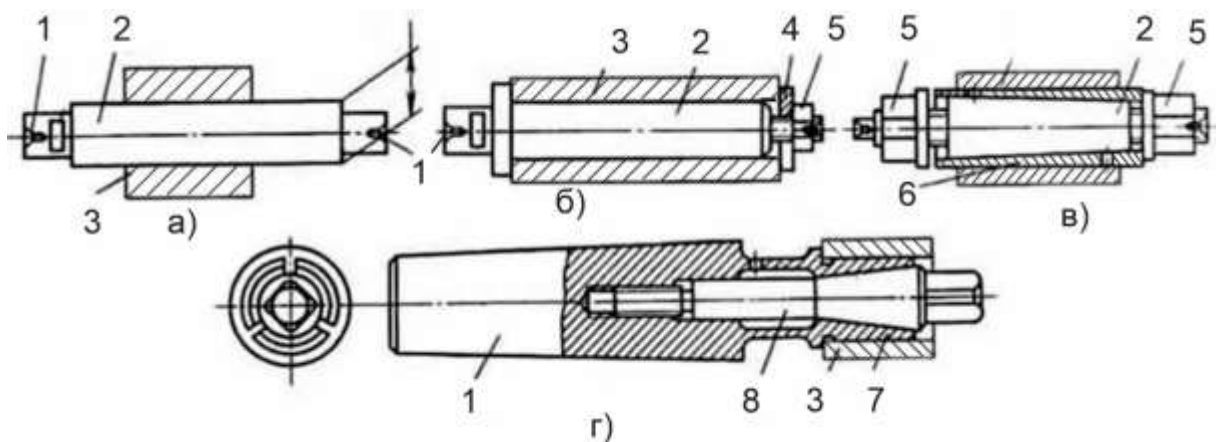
Схеми встановлення заготовок на оправках під час обробки зовнішніх циліндричних поверхонь.
